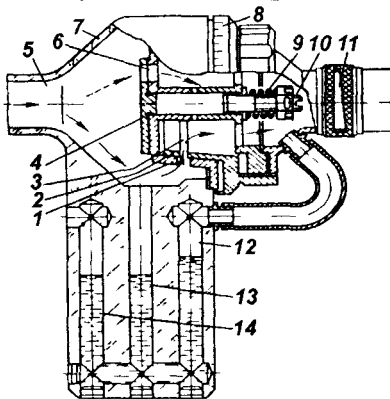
Схема приладу КИ-4887-1: 1 – нерухома втулка; 2 – рухома втулка; 3 – дроселюючий отвір; 4 – заслінка; 5 – впускний трубопровід; 6 – калібрований отвір; 7 – корпус; 8 – шкала витрат; 9 – пружина; 10 – випускний парубок; 11 – дросель; 12, 13, 14 – рідинні манометри
